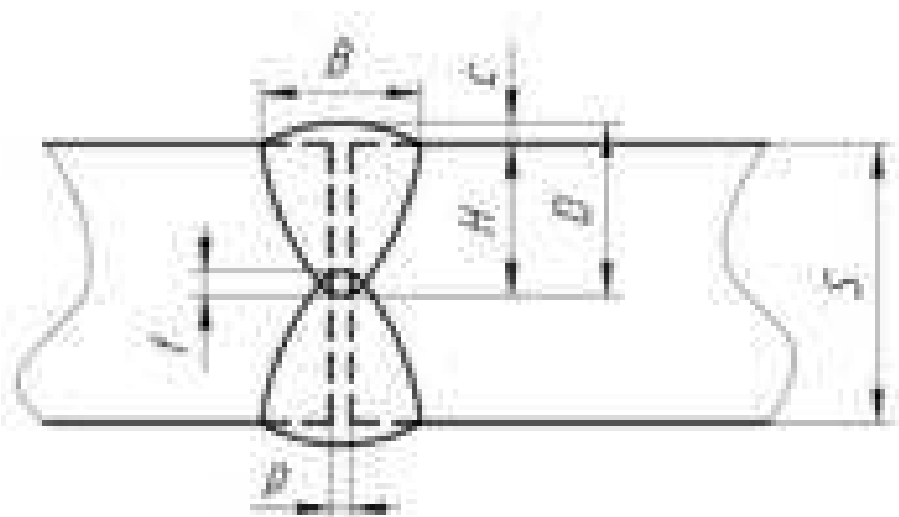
Обеспечение полного провара соединяемых пластин.
